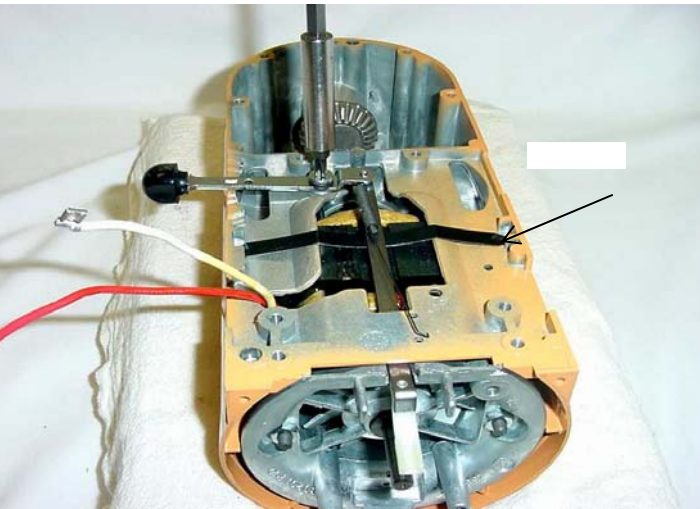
Drehpunktschraube und Spannscheibe mit Kreuzschlitzschraubendreher entfernen.
